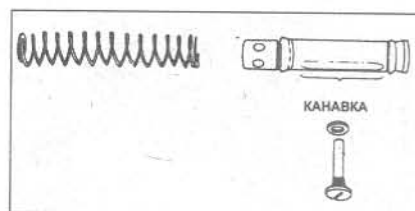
Установочные детали сборки поршня главного цилиндра (Глава 7)
